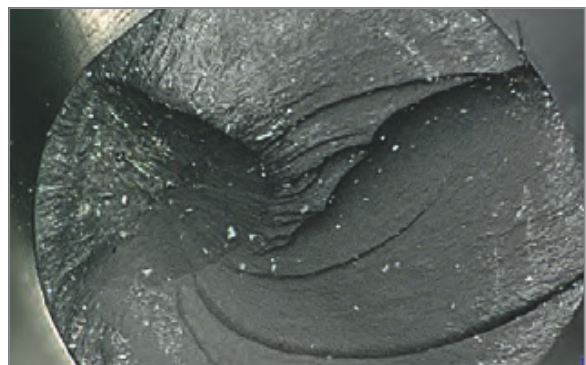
Bruchfläche eines durch Spirallrisse ausgefallenen O-Rings – gut erkennbar ist die erfolgte Torsionsbeanspruchung des Querschnittes
